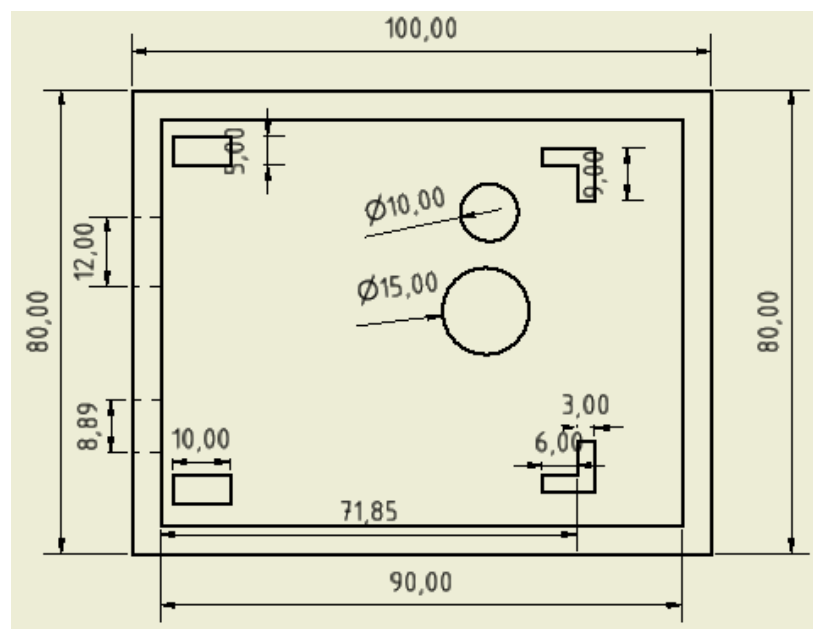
Planos caja Arduino parte uno. (Fuente los autores).
